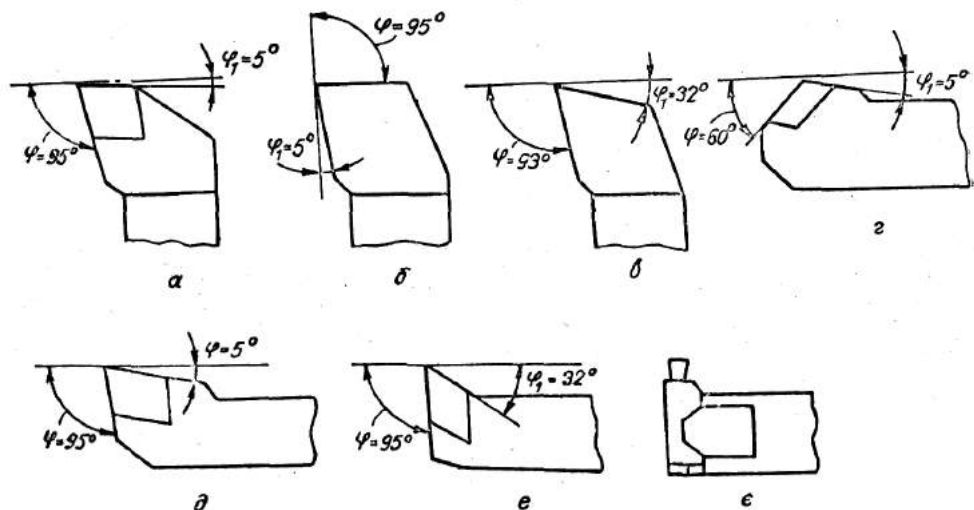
Комплект різального інструменту для токарних операцій: а — прохідний упорний чорновий; б — підрізний; в — контурний чистовий; г — розточувальний чорновий; д — розточувальний упорний чорновий, е — розточувальний контурний чистовий; є — канавковий внутрішній.
